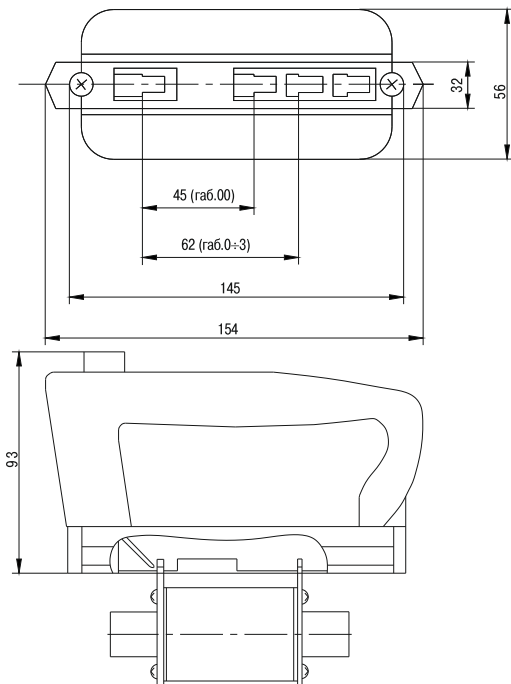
Габаритные размеры рукоятки для смены плавкой вставки
